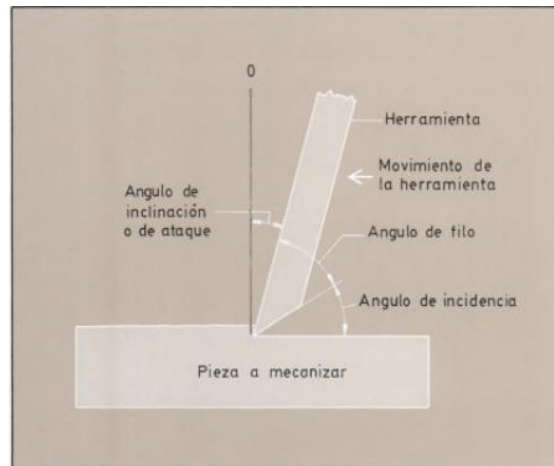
Posición relativa de la herramienta de corte y la pieza a mecanizar
